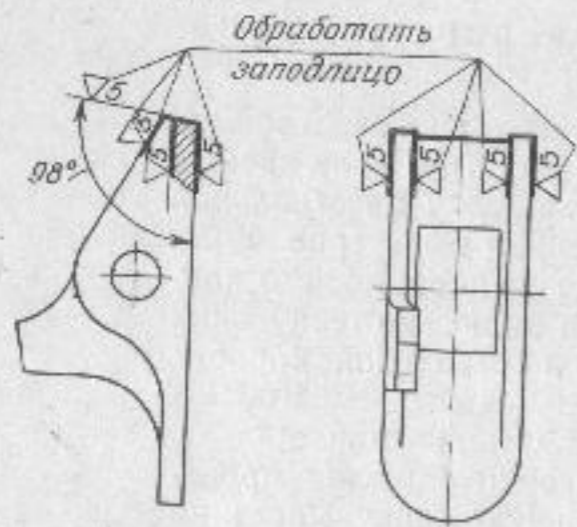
Обработка верхнего торца защелки магазина после наплавки
